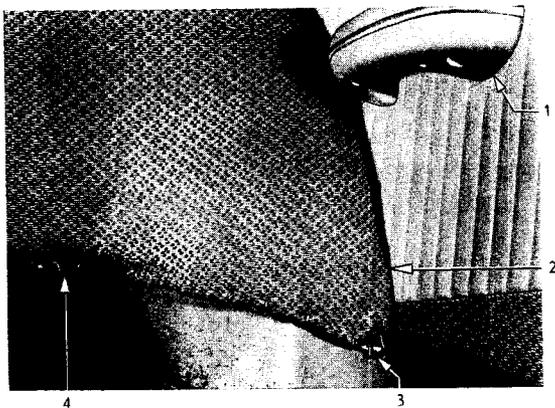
Untere Befestigung der Hintersitz-Rückenlehne
